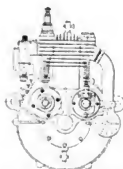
Dürkopp-Vierzylindermotor, Ansicht von vorn.
